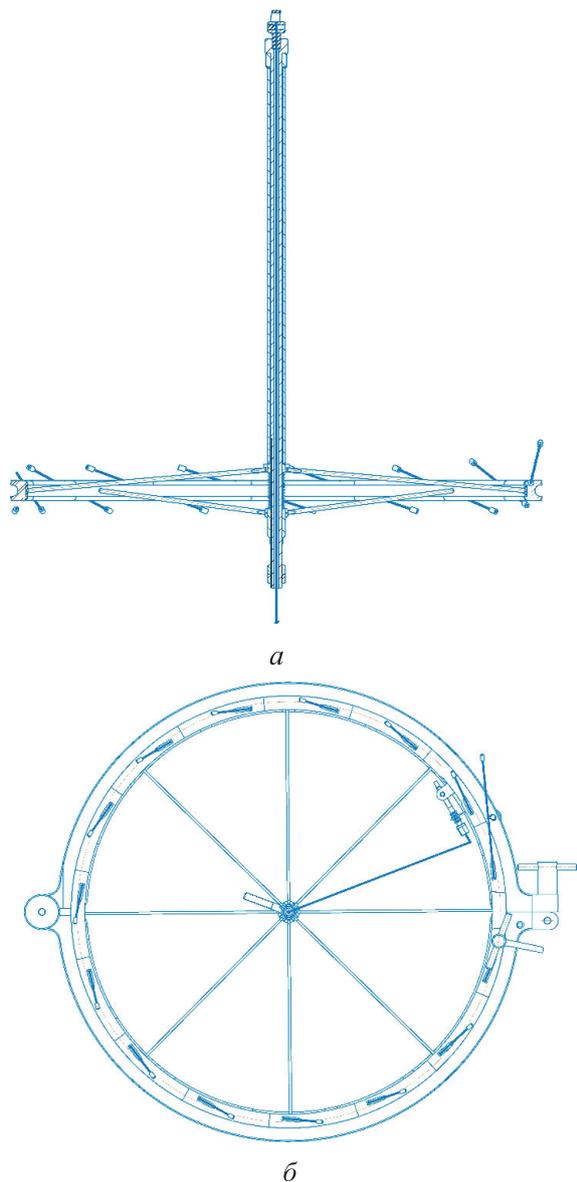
Схемы приспособления для защиты от сварочных брызг и подплавления внутренней поверхности полусфер:
